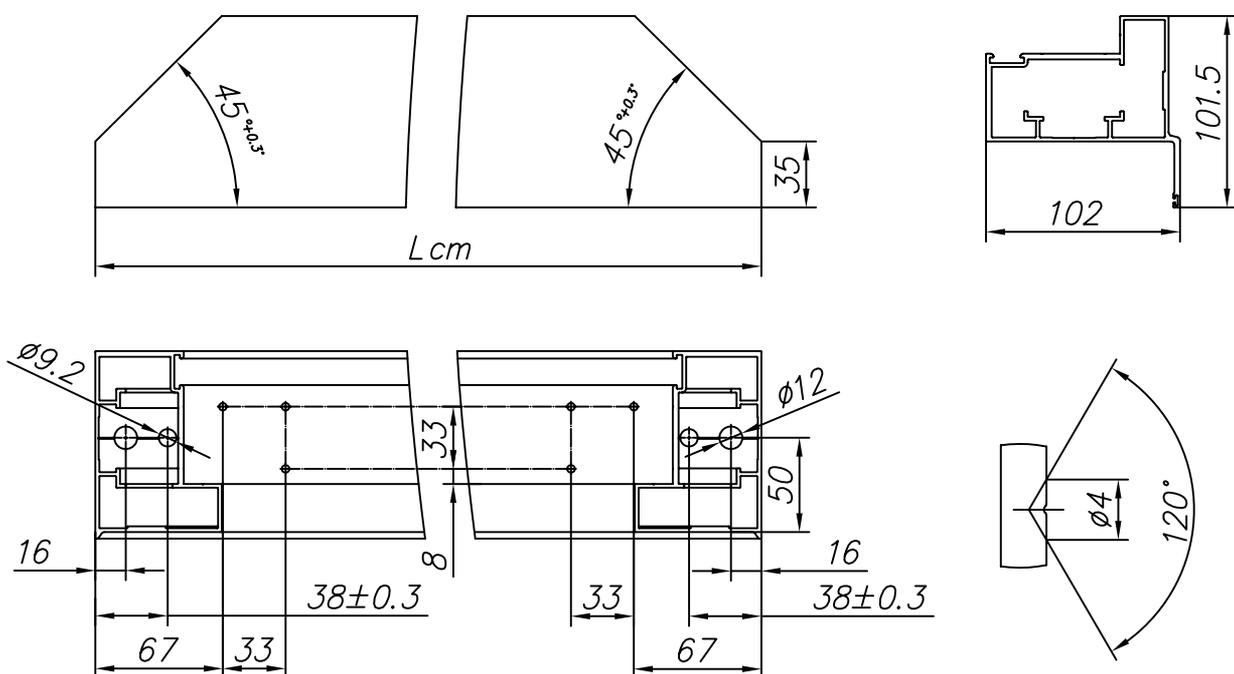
Изготовление стойки (профиль рамы FLGU.400.0116)
